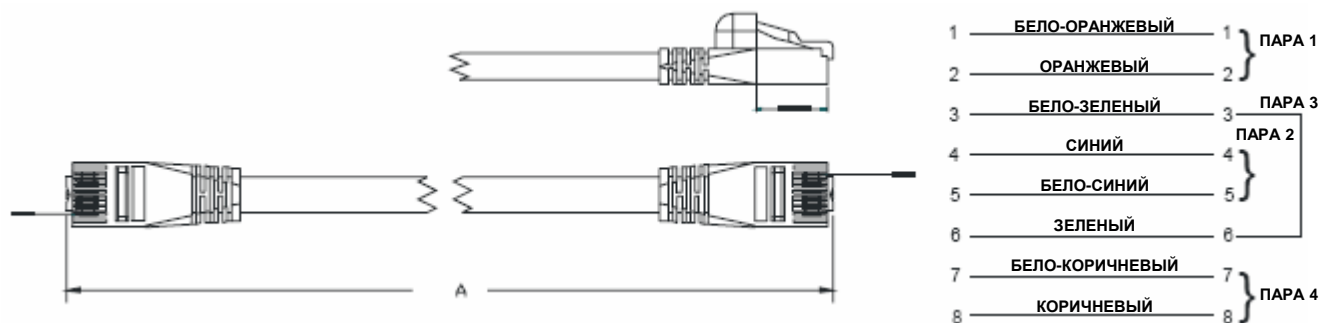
Стандартный Кабель Ethernet (Кат. 5)
